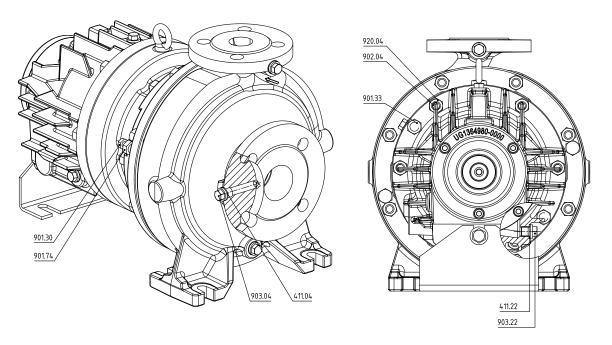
Крепление крышки с напорной стороны на корпусе насоса для исполнения с привинчиваемой крышкой корпуса Варианты конструкции
